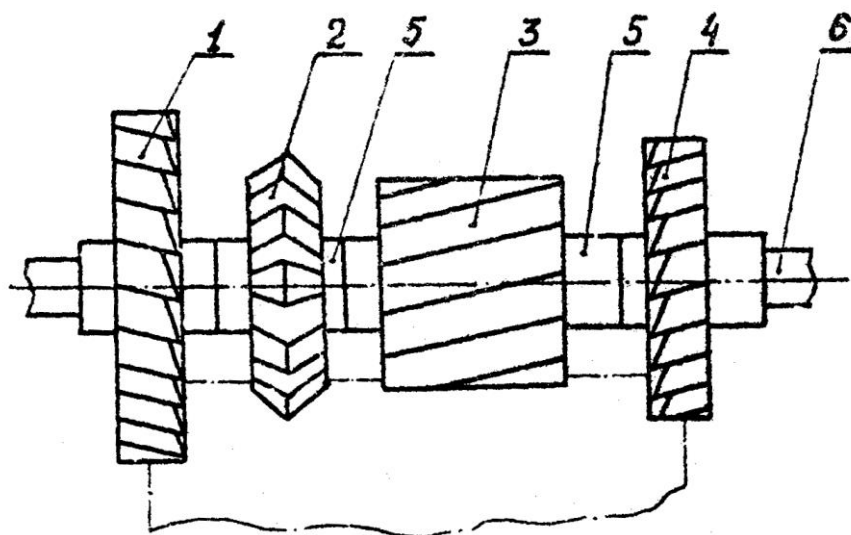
Блок фрез: 1, 2, 3, 4 – набор фрез;
